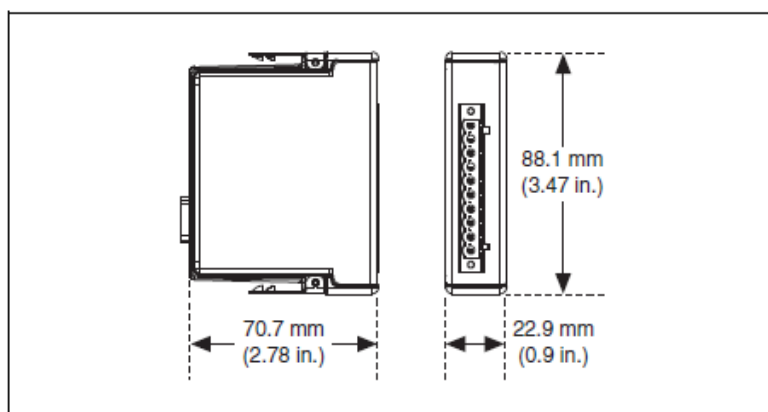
Serie C de E / S del módulo, Vista frontal con Dimensiones
